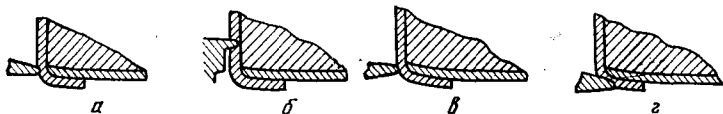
Схемы обжима заготовки верха обуви губками матрицы
